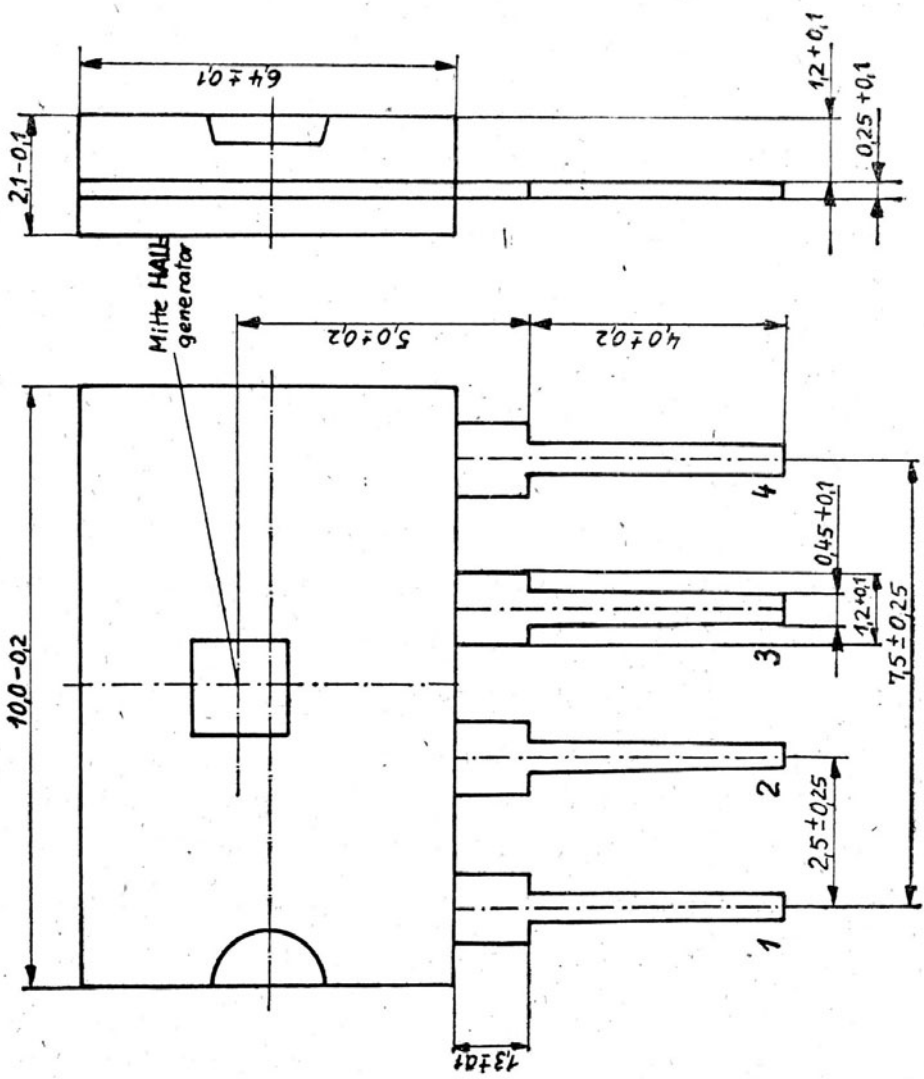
Mechanische Gehäuseskizze des B 461G/B 462 G
